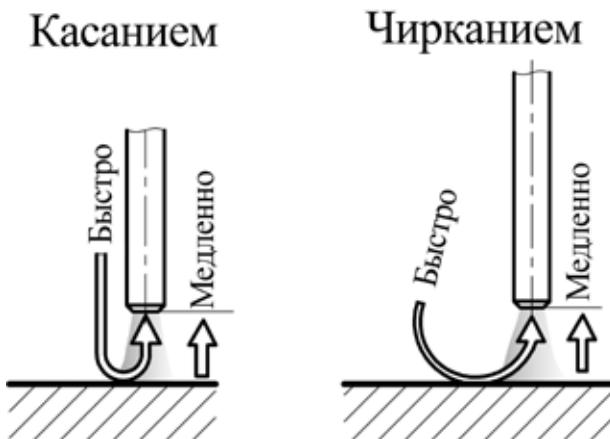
Способы зажигания сварочной дуги.
